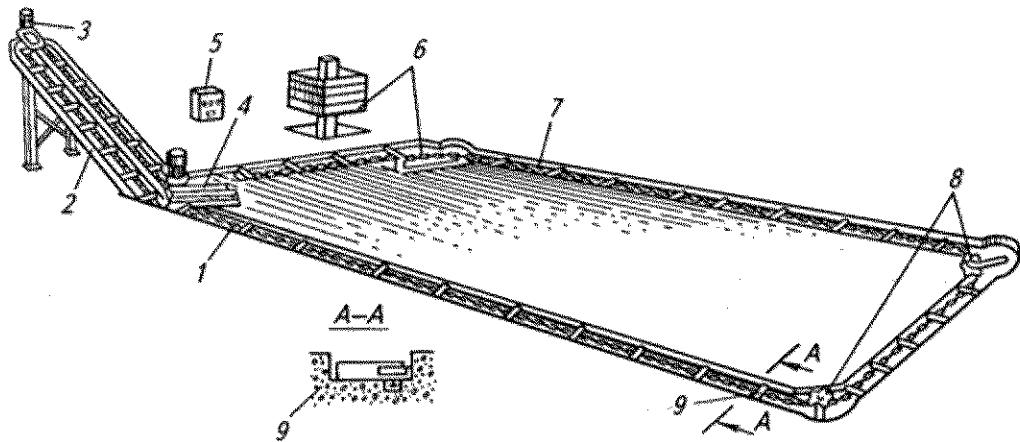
Схема скребкового транспортера ТЧН–160А:
